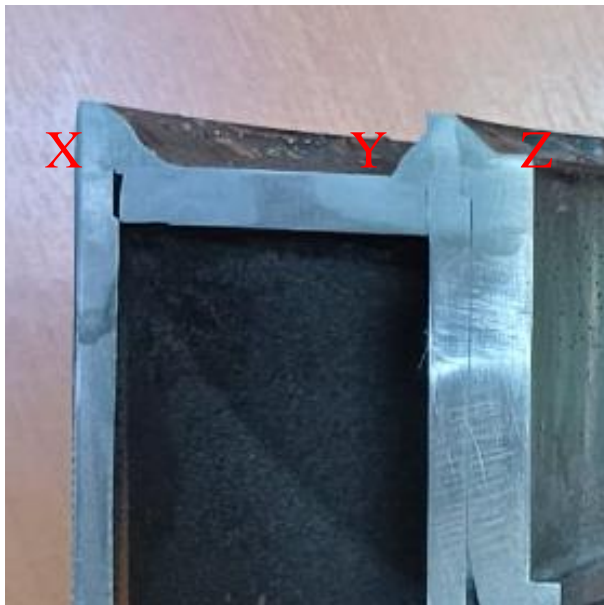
corpo de prova 3 solda X, Y e Z.
